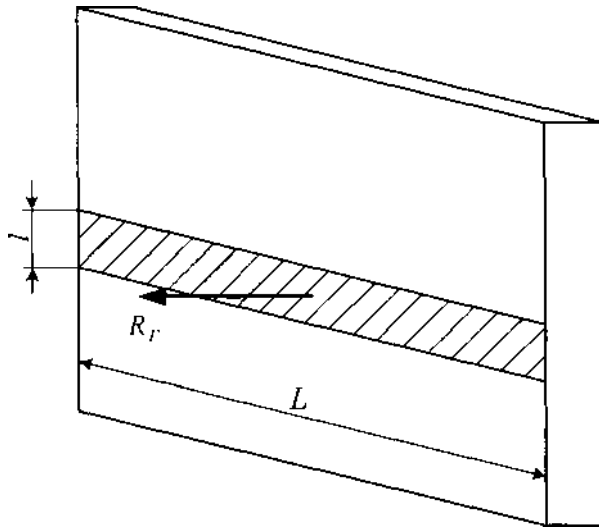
Нерухома щока одновалкової дробарки
